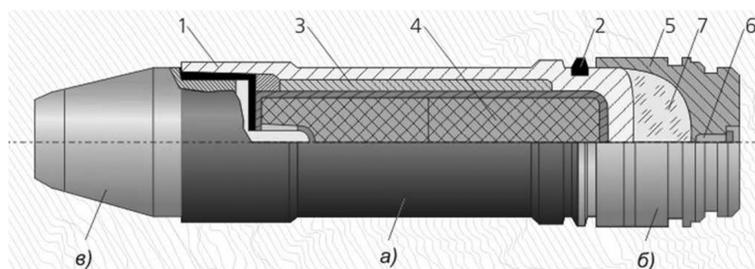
Гранатометный выстрел ВОГ-17М: а — осколочная граната; б — пороховой заряд; в — взрыватель; 1 — корпус; 2 — ведущий поясик; 3 — пружина (осколочная рубашка); 4 — разрывной снаряд; 5 — гильза; 6 — капсюль-воспламенитель; 7 — нитроглицериновый порох
